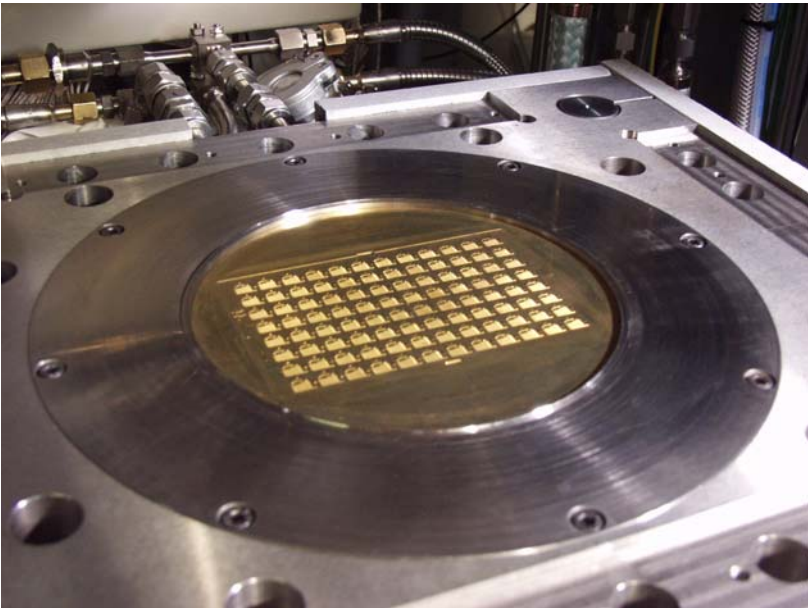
Ansicht der Werkzeugunterhälfte
